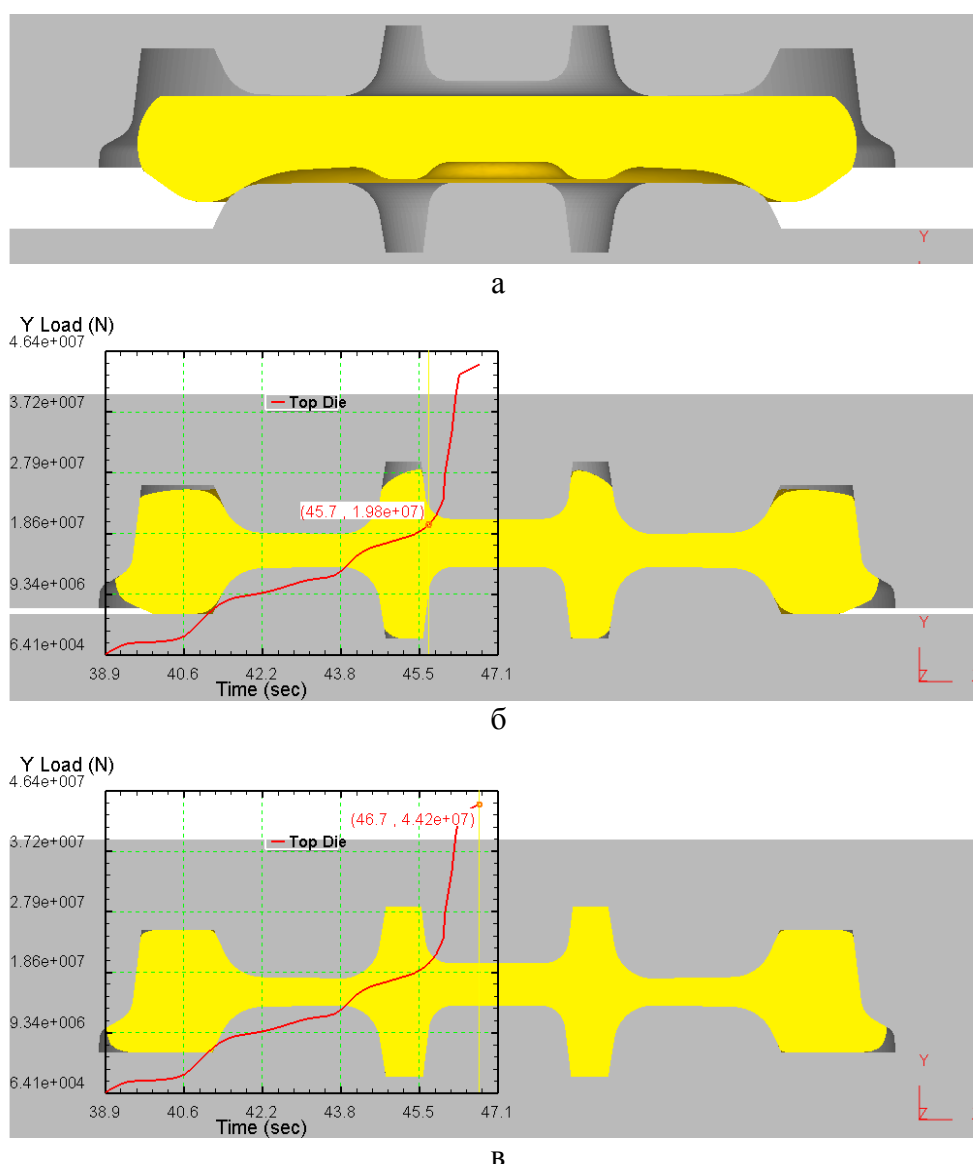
Штамповка колёсной заготовки по схеме Б:
